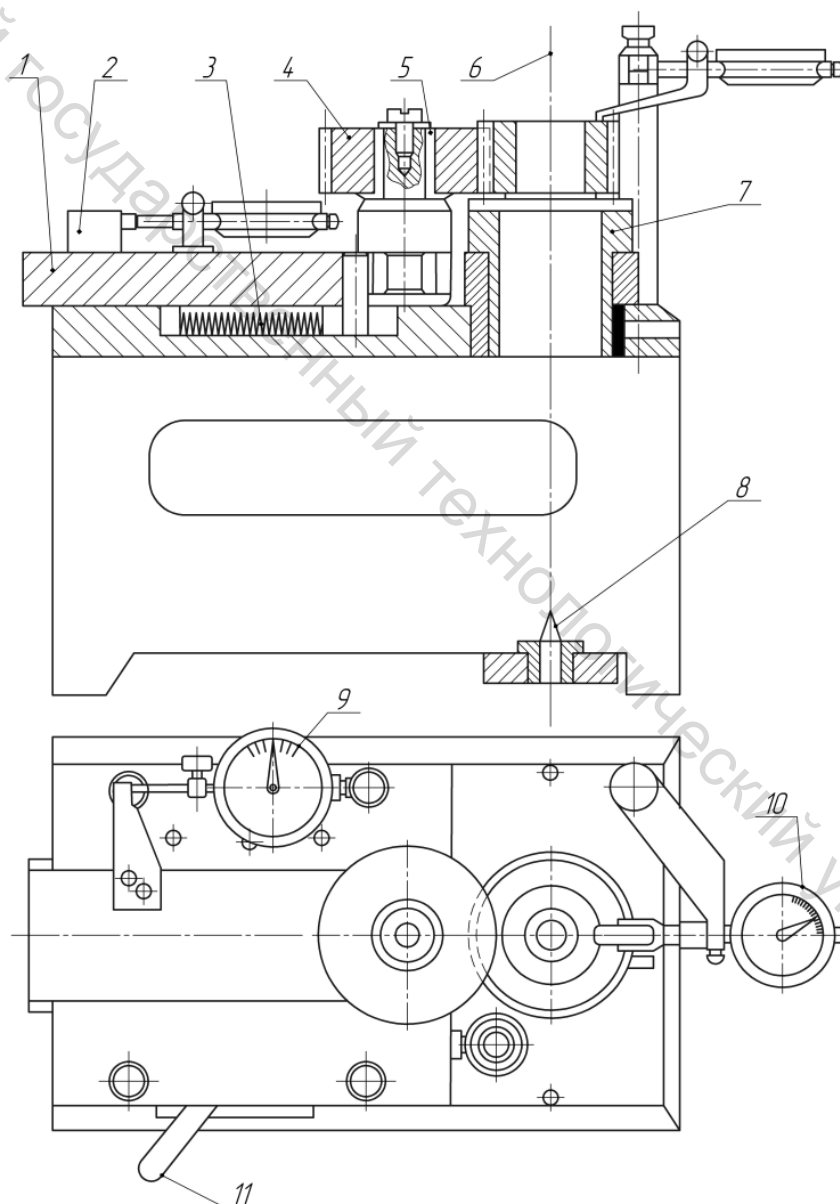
Контроль пары «зубчатое колесо – вал» в крупносерийном и массовом производствах
